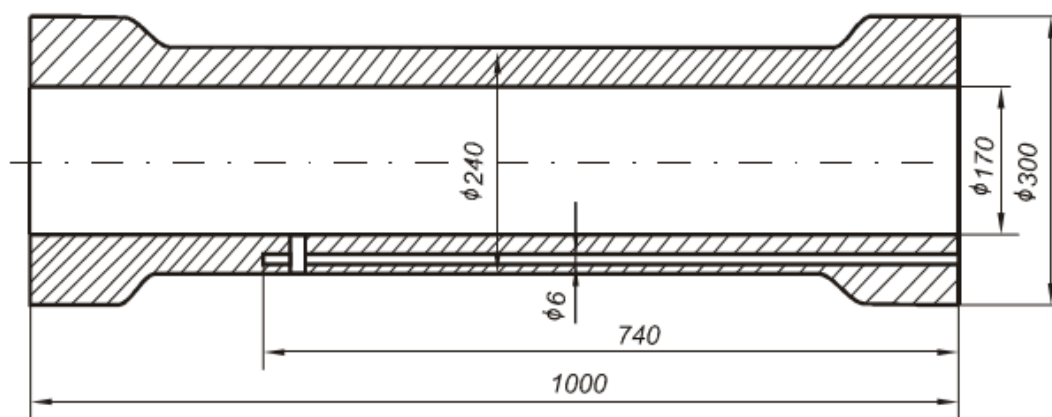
Пример нетехнологичной конструкции корпуса гидравлического цилиндра
